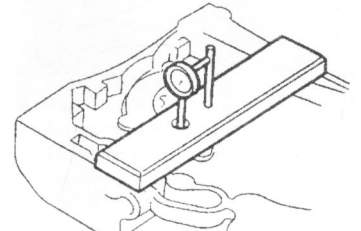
С помощью циферблатного прибора измерить торцевой зазор шестерен.
